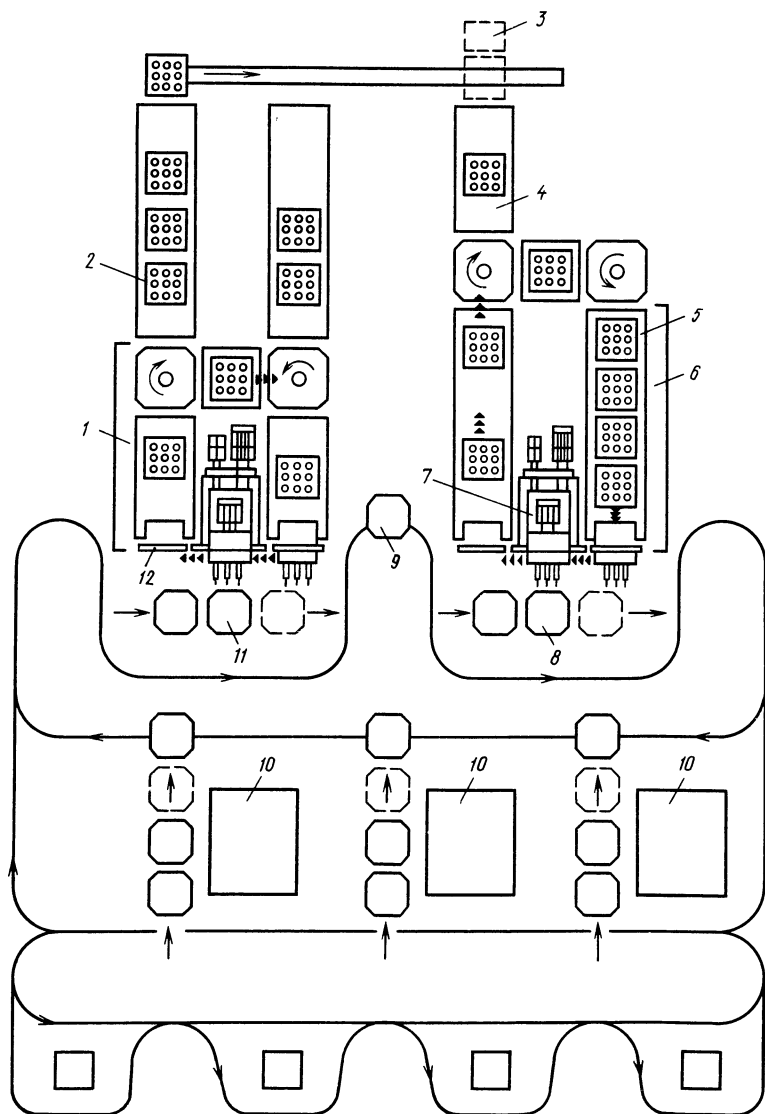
Компоновка ГАЛ со сменными шпиндельными коробками
